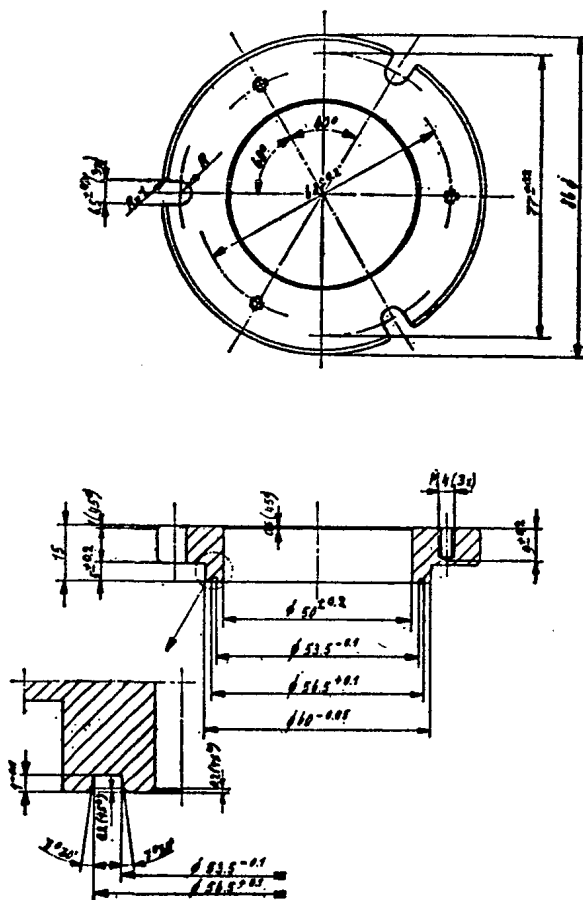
Anello di pressione del recipiente; dettagli in sezione verticale ed in pianta (dimensioni in mm)
